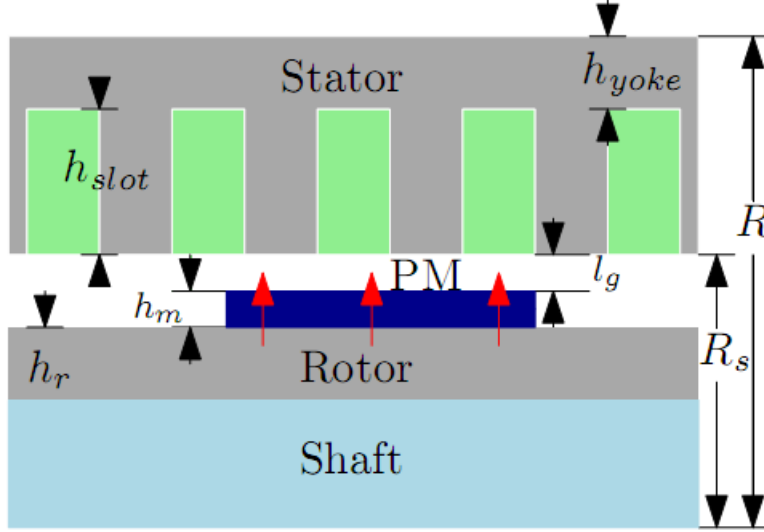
Dimensions principales de la génératrice pentaphasée
